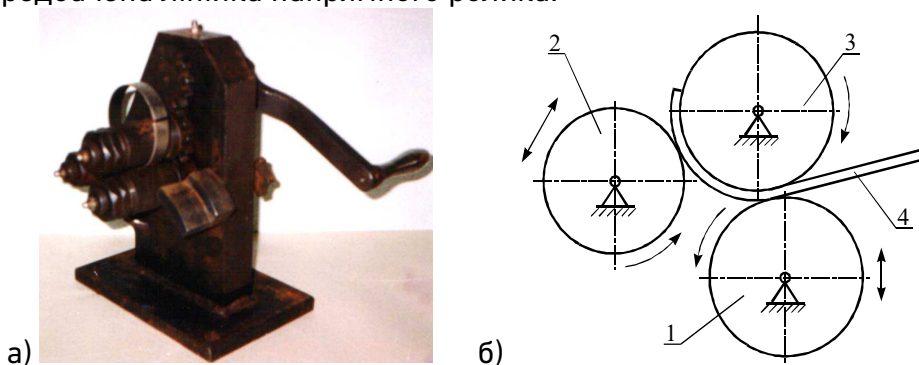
Загальний вигляд (а) роликового валкового пристрою для згинання пластини у втулку та принцип формування необхідного радіусу вигину втулки (б)
